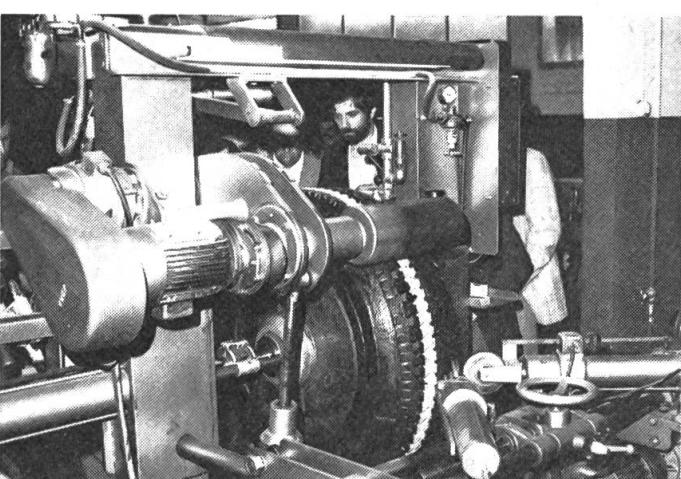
Procédé Vacuum-Vulk. Machine à coller la nouvelle bande de roulement sur la carcasse.
